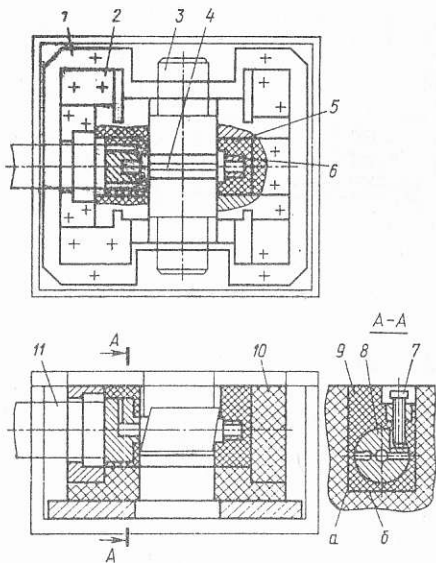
Приспособление для ЭХО лопаток с предварительно установленными базовыми элементами
